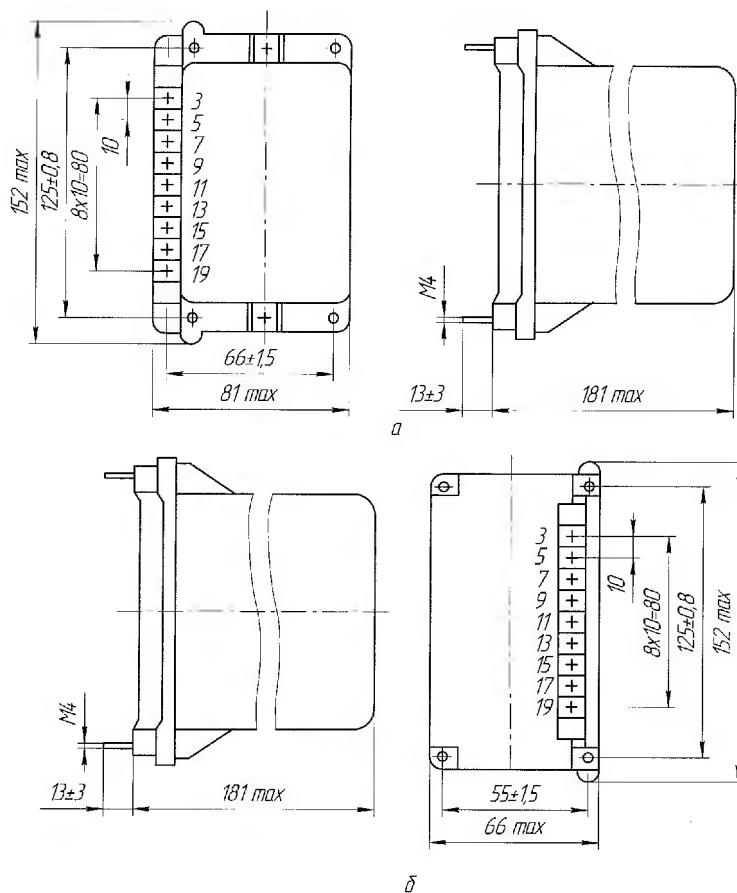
Габаритные, установочные и присоединительные размеры реле РВ 03.
